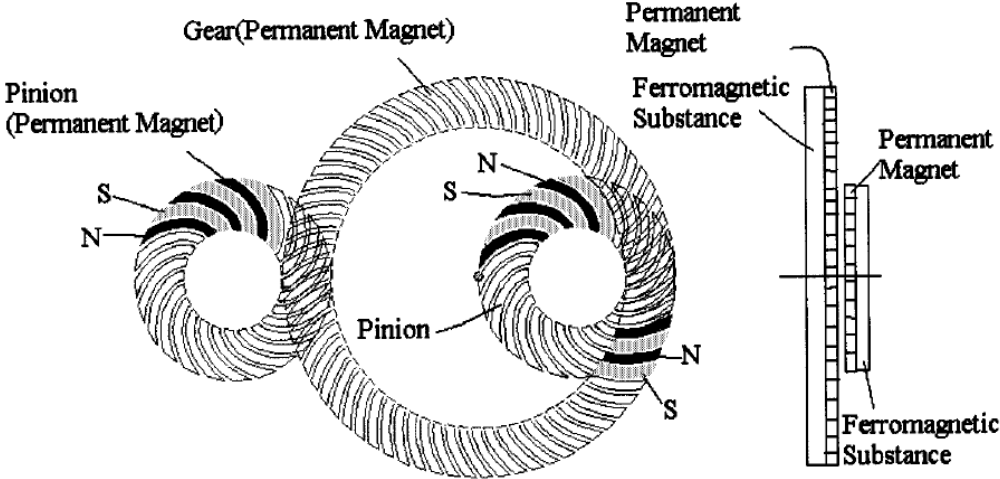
Engrenage magnétique à denture hélicoïdale à disque axial [TK87]
